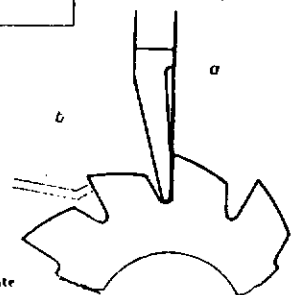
,1. Afilado de una fresa cilíndrica. a) Muela frontal; b) apoyo de los dientes.
